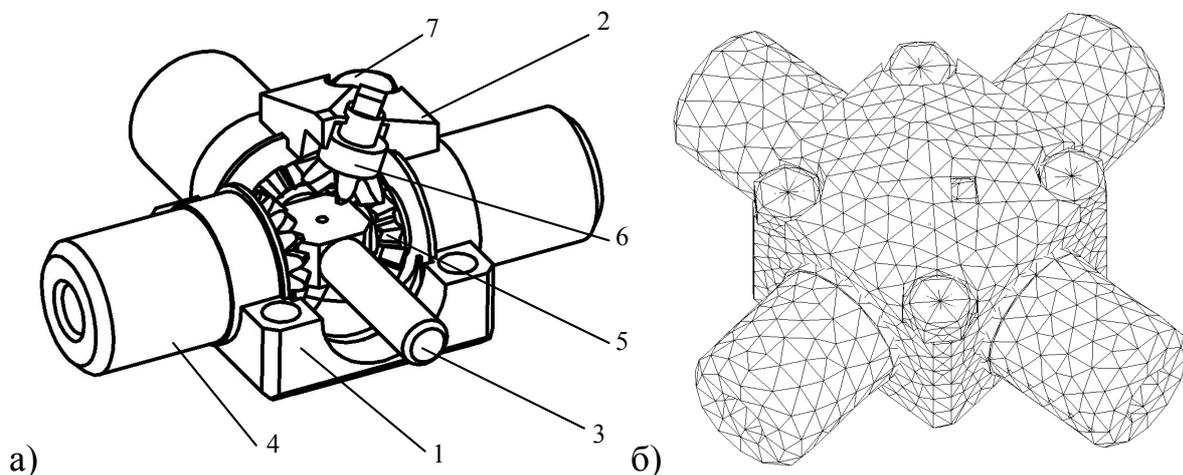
Крестовина карданного шарнира (RU 2238446): а) схема крестовины; б) конечно-элементная модель крестовины; 1 – нижний корпус; 2 – верхний корпус; 3 - центрирующий элемент; 4 – шипы; 5 - конические зубчатые колеса; 6 – приводной элемент; 7 – винты
